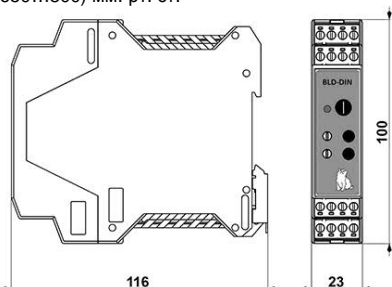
Габаритные и присоединительные размеры блока BLD-20DIN.
